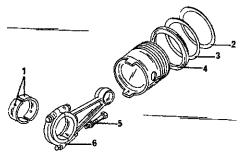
Монтажный чертеж поршня вместе с шатуном на двигателе с рабочими гильзами цилиндров.
